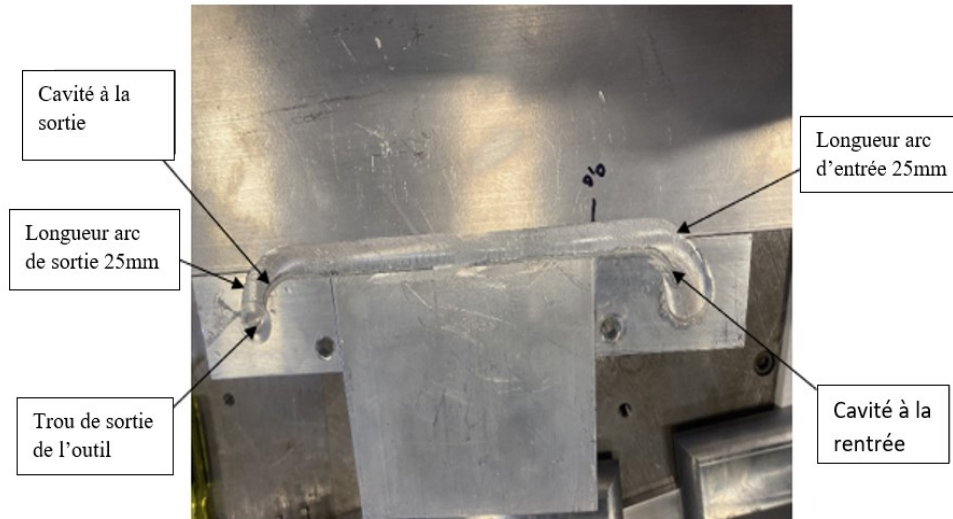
Les conditions de soudages utilisées avec 25 mm de rayon à l'entrée et à la sortie de deux poutrelles
